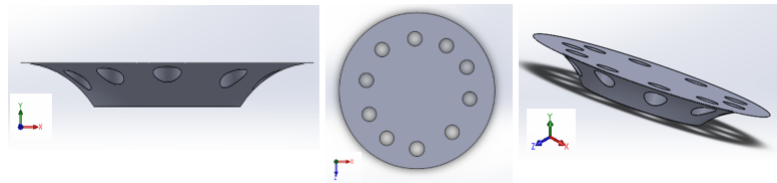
Adaptador projetado para unir cilindro linear com o cilindro rotativo, em vista frontal, superior e isométrica, respectivamente.
